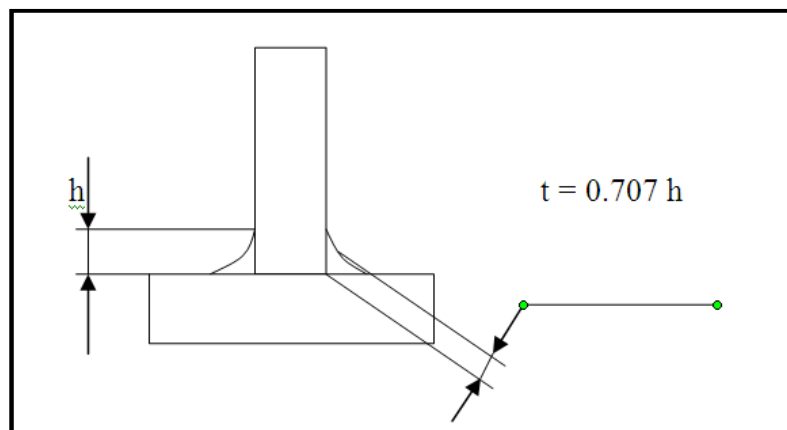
Representación de la altura y espesor de cordón de soldadura.
